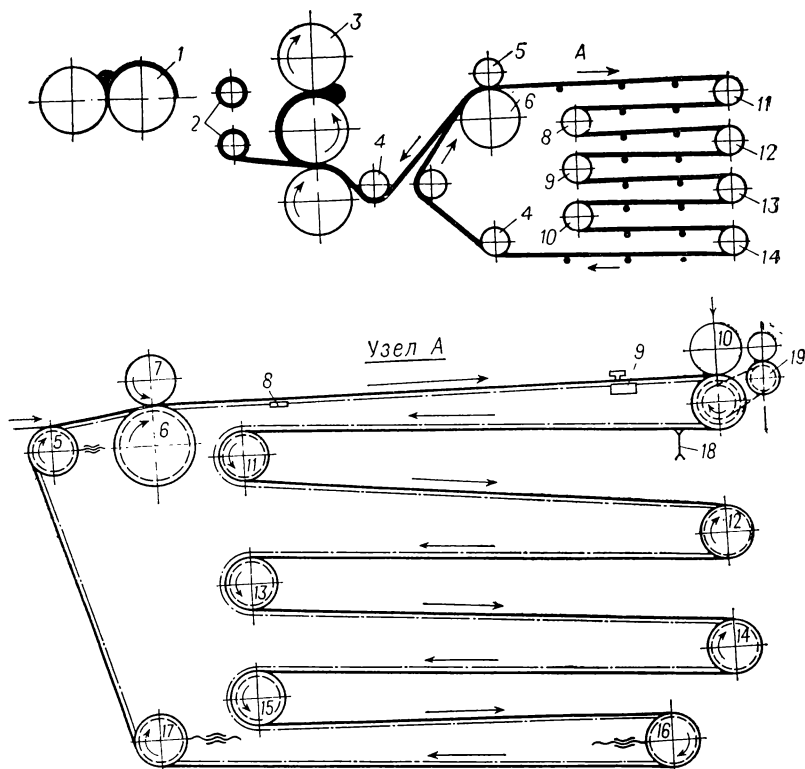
Схема технологического процесса сборки ремневых пластин на дублировочном агрегате:
